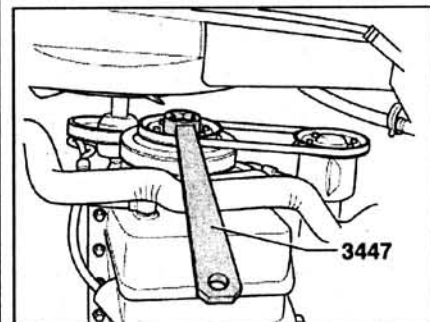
Установите ключ 3447 на центральный болт шкива коленчатого вала и заблокируйте коленчатый вал от вращения. Открутите болт крепления шестерни распределительного вала и снимите его.
